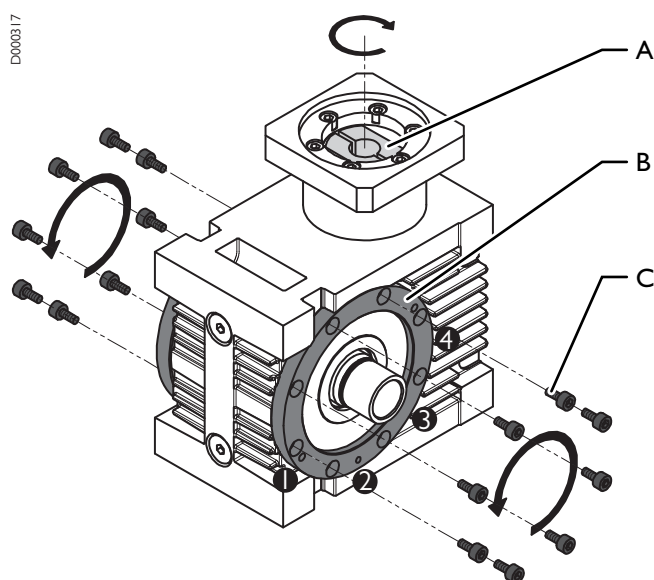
Выставить зазор в редукторе: Блок редуктора GÜdel
